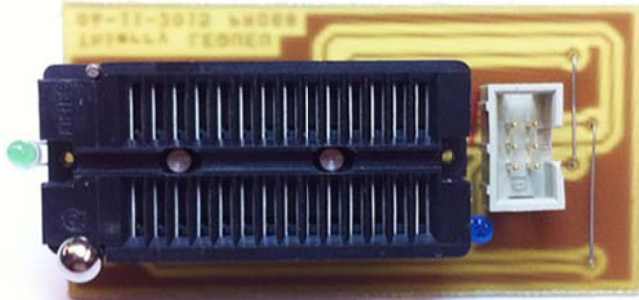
Vue d'ensemble du montage (images-composants\PROG08-13, 32 & 33.jpg).
